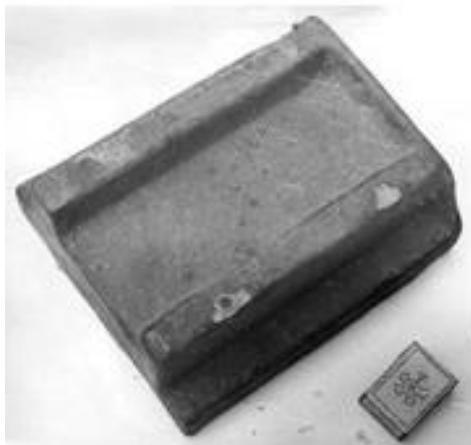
Электрошлаковая отливка заготовки базовой плиты УСП
